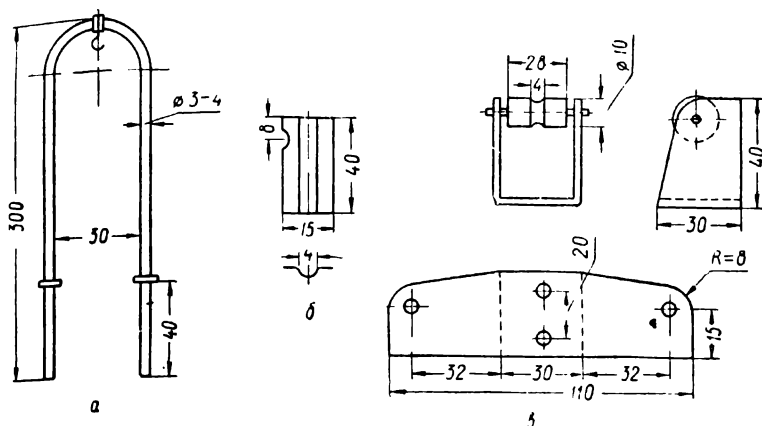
Детали устройства стойки, гнезд для нее и блока
